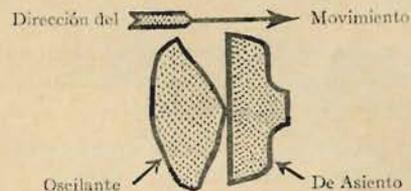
Modo de Colocar el Pasador Oscilante y el Pasador de Asiento
